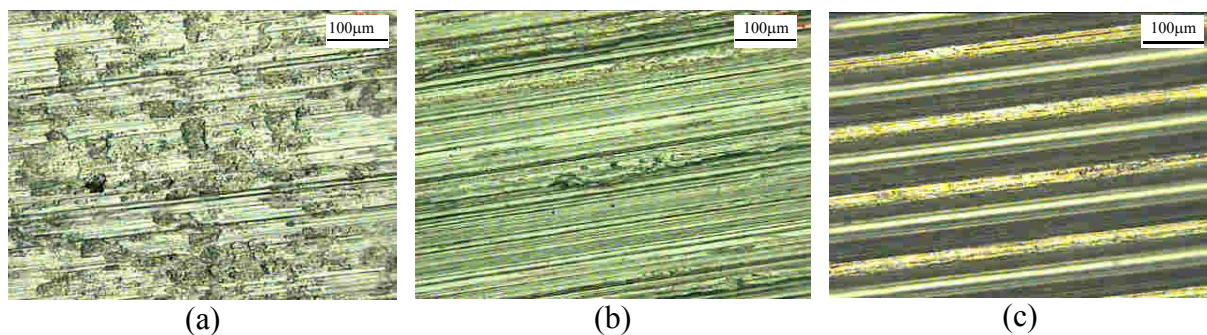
Superfícies usinadas com profundidade de corte de 0,1 mm dos aços (a) 303, (b) 304 e (c) 310. Microscopia óptica.
